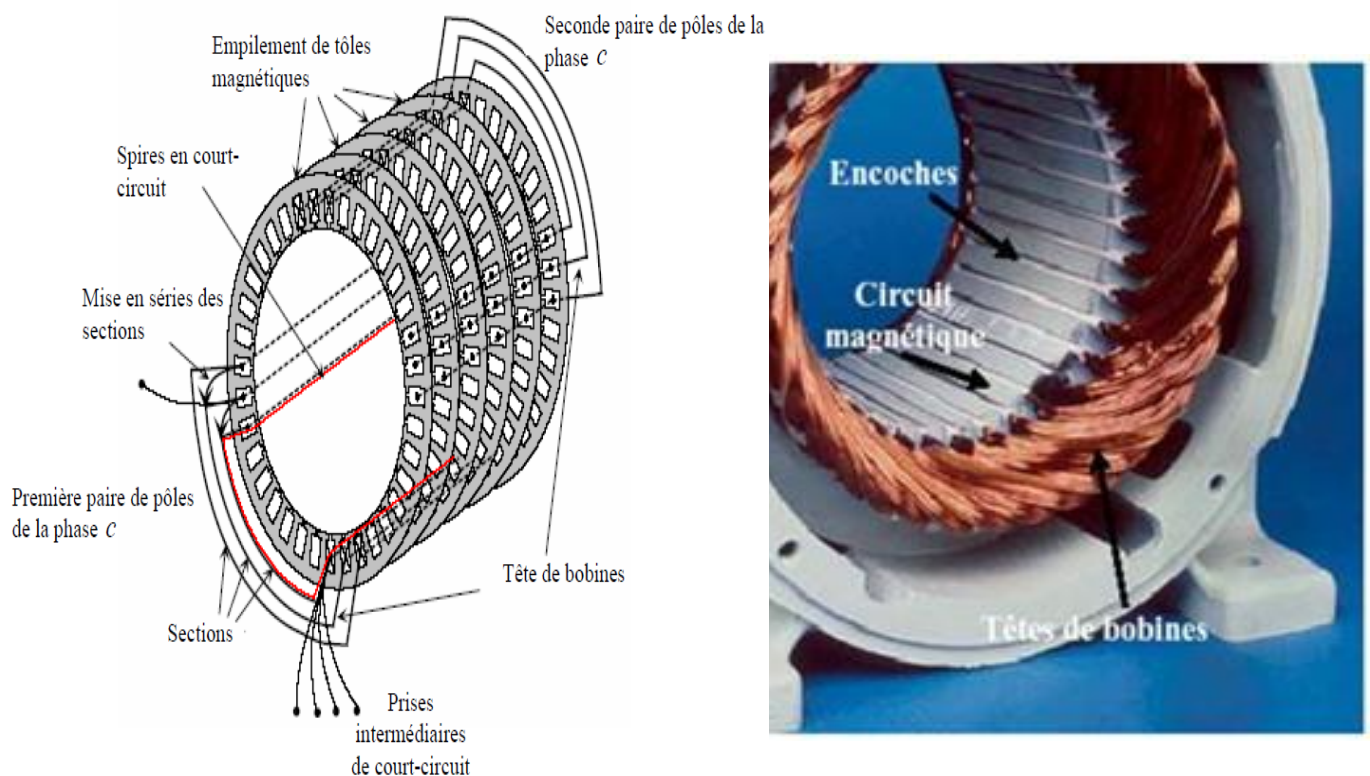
Différentes composantes de la machine asynchrone à cage [6].
